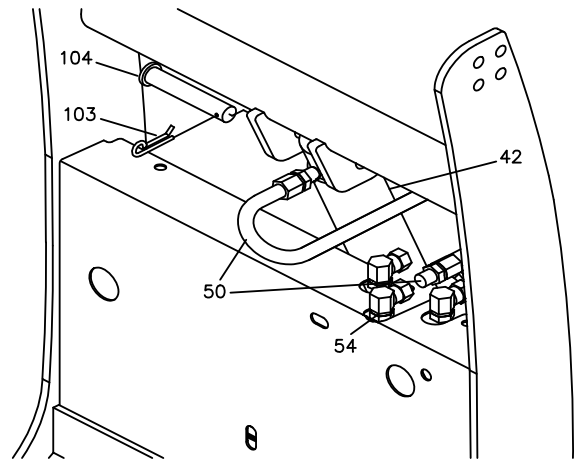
Montage Hebe Zylinder Hydraulik. G10138
